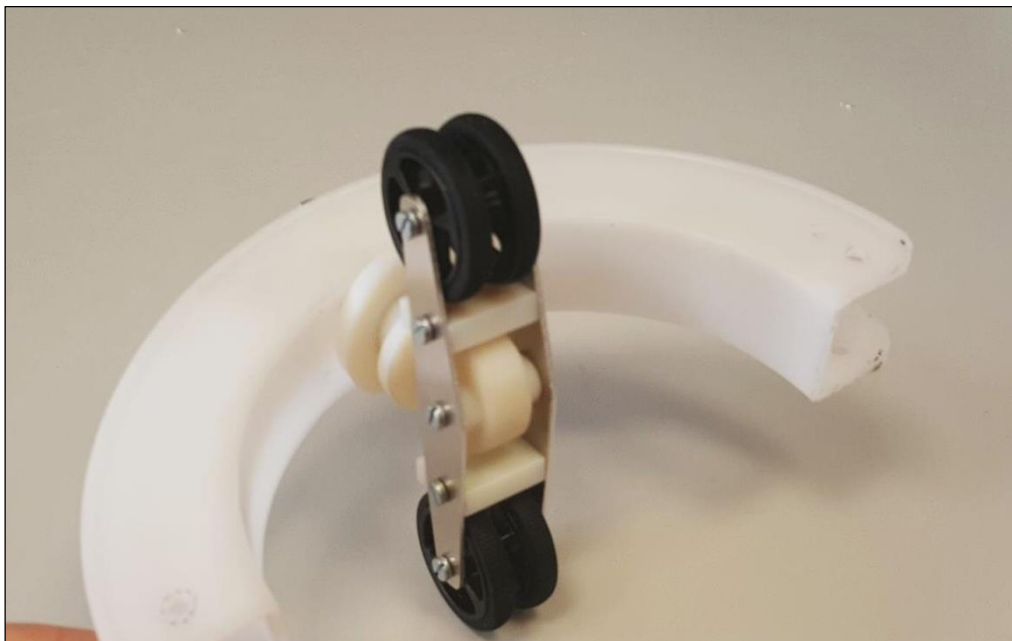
Montaje Eje Motriz – Acoplamiento Motor
